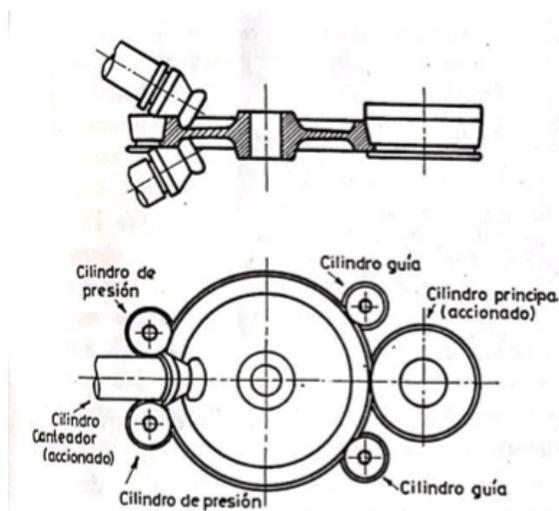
Alzado y planta mostrando la disposición esquemática de los cilindros en un laminador horizontal de ruedas.
